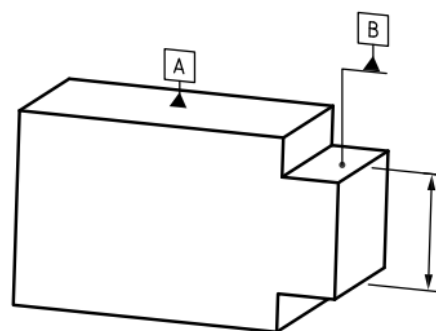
Κενό τριγωνικό σύμβολο datum
